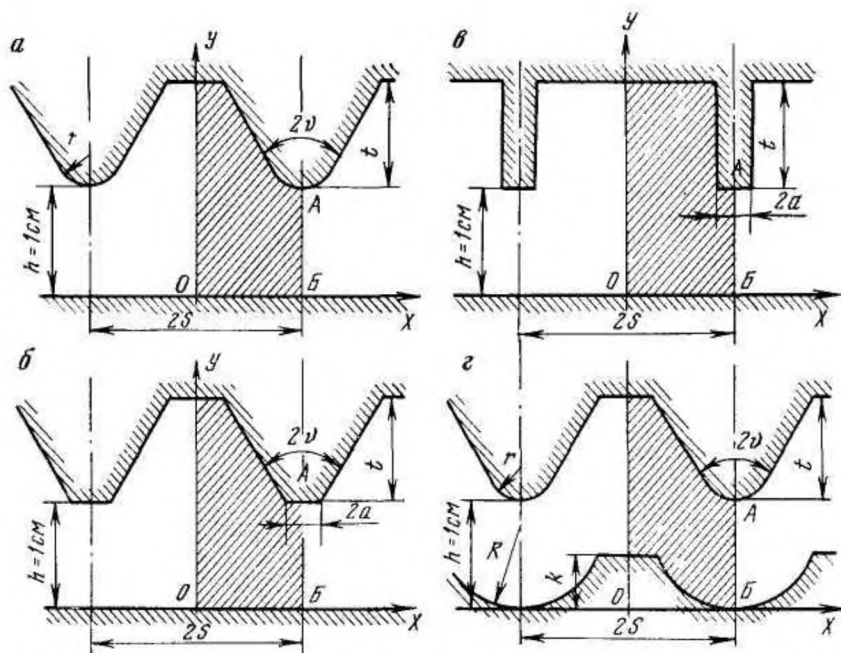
Основные профили рабочих зон сепараторов с сильным полем: а — закругленный зубец — плоский полюс; б — трапецеидальный зубец — плоский полюс; в — прямоугольный зубец — плоский полюс; г — закругленный зубец — желобчатый полюс.
